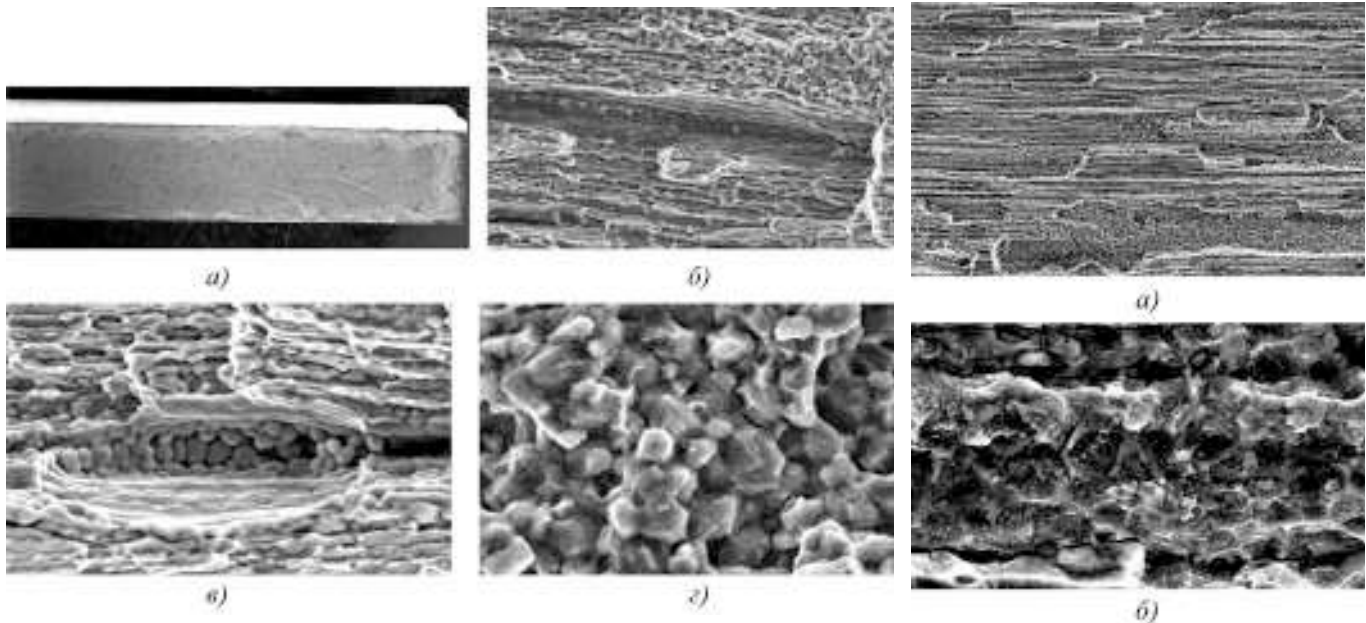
Строение излома сварного соединения прессованной полосы толщиной 40 мм, верх шва:
